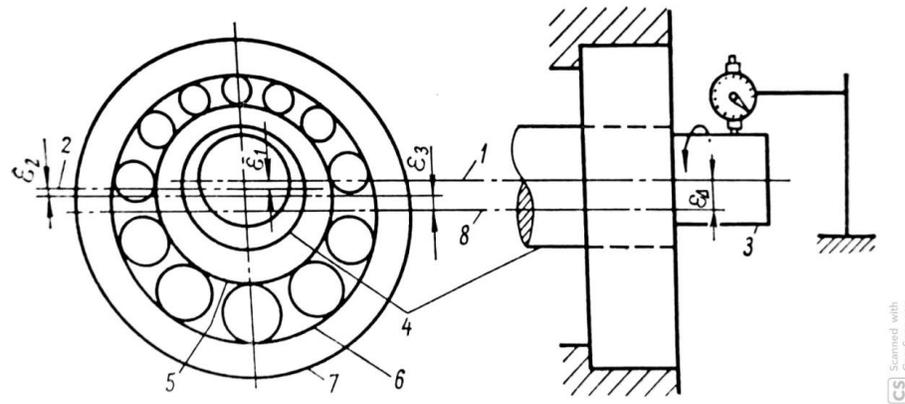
Control de la coaxialidad del husillo de una máquina herramienta
